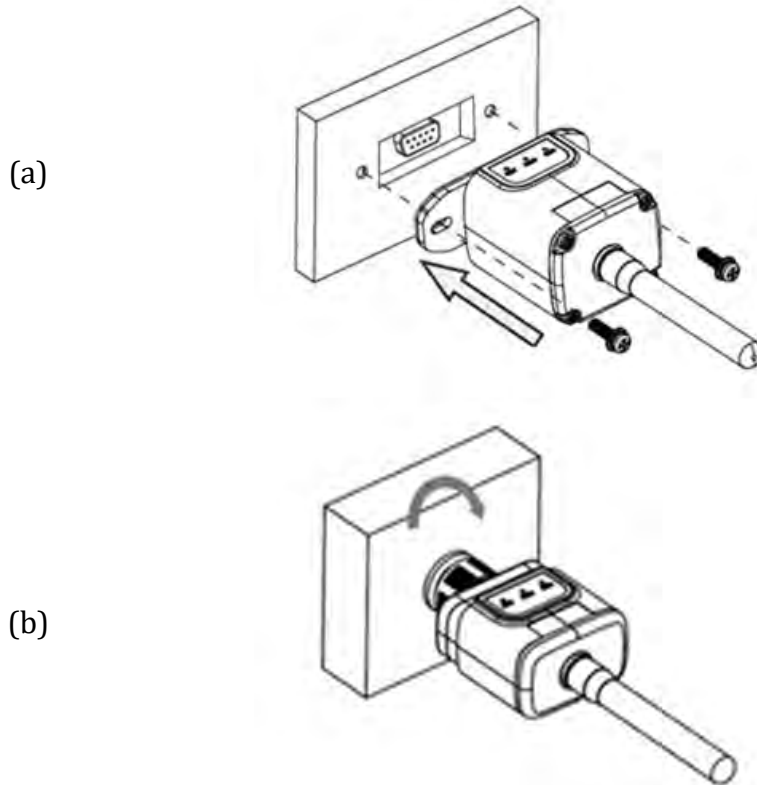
Inserimento e fissaggio dell'adattatore 4G
